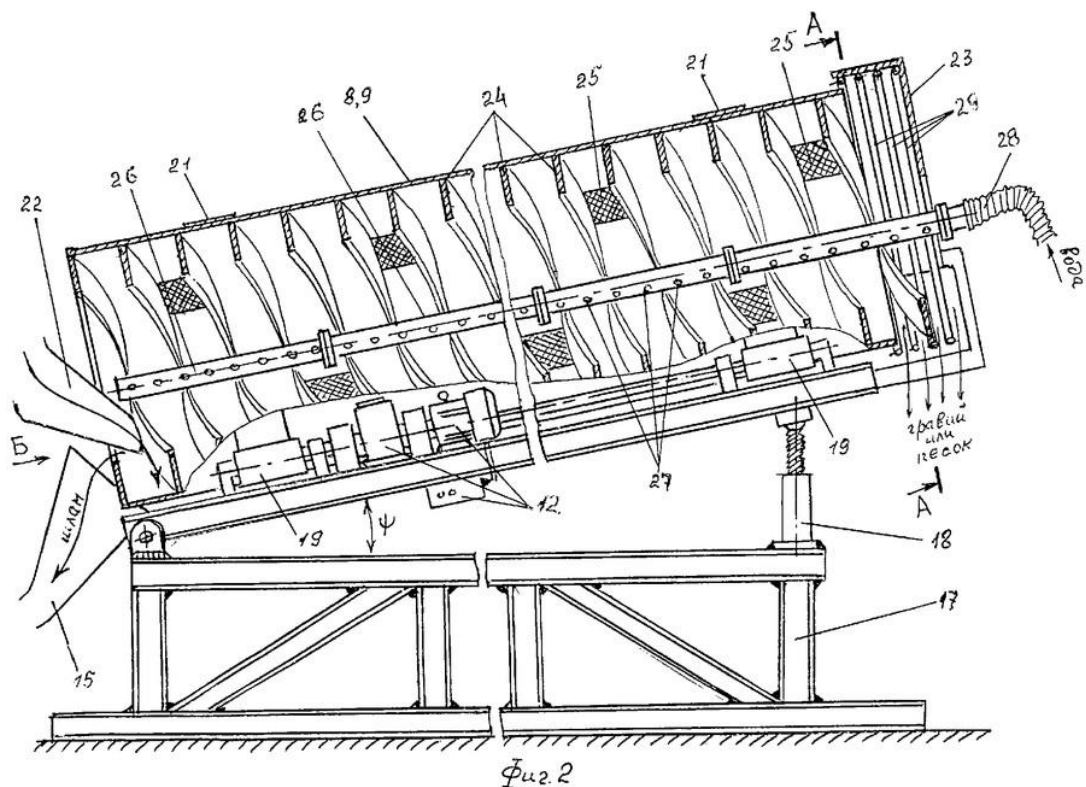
Устройство для выборки глины и очистки песка и гравия.
